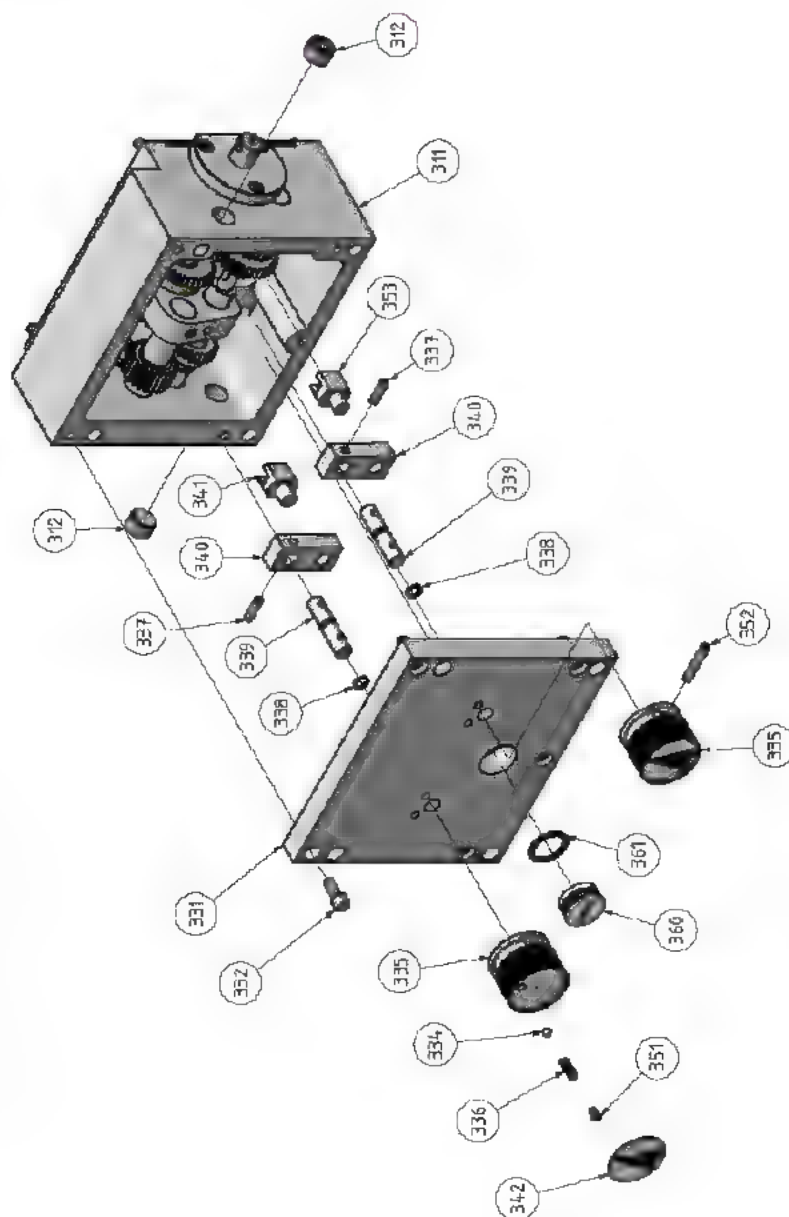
Vorschubgetriebe D280 1 von 2 - Feed gear D280 1 of 2
